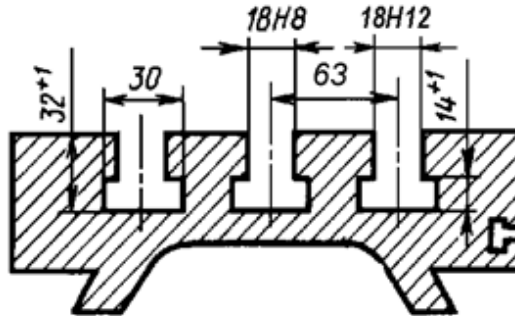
Посадочні розміри робочого столу вертикально фрезерного верстату моделі 6Т12
